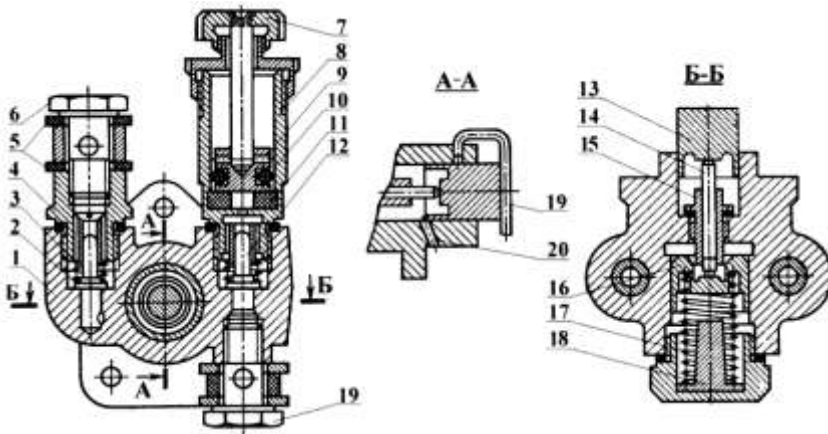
ТПН модели УТН-3 производства НЗТА: 1 - корпус; 2,12 - клапан-грибок; 3,17 - пружина; 4 - футорка; 5 - прокладка; 6,19 - болт-штуцер; 7 - рукоятка ручного насоса; 8 - ручной насос; 9 - поршень ручного насоса; 10 - кольцо; 11 - прокладка; 13 - толкатель; 14 - шток толкателя; 15 - прецизионная втулка; 16 - поршень; 18 - вытеснитель; 19 - предохранительная чека; 20 - дренажное отверстие.
